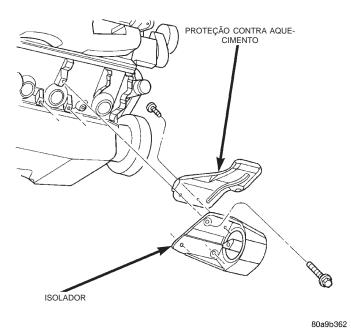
Montagem do Isolador Dianteiro Direito do Motor — Veículos 2WD
